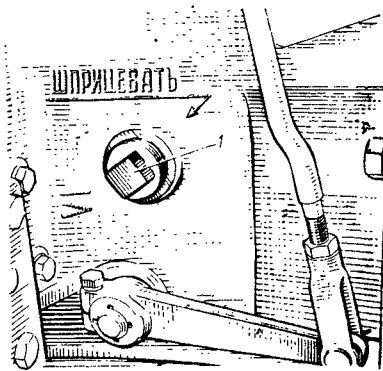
Смазывание подшипника отводки муфты сцепления:
